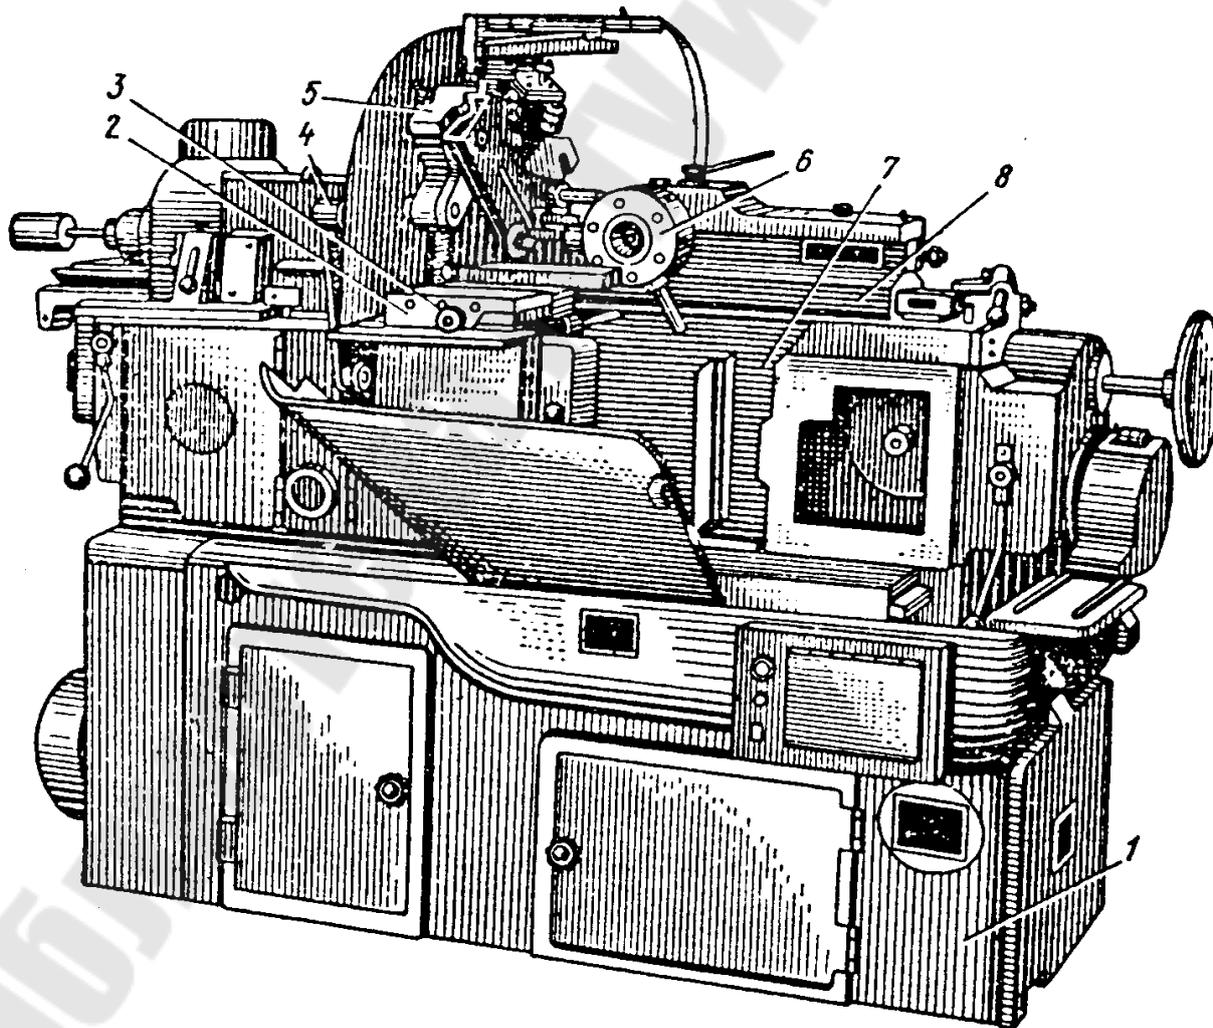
Общий вид токарно-револьверного одношпиндельного автомата
